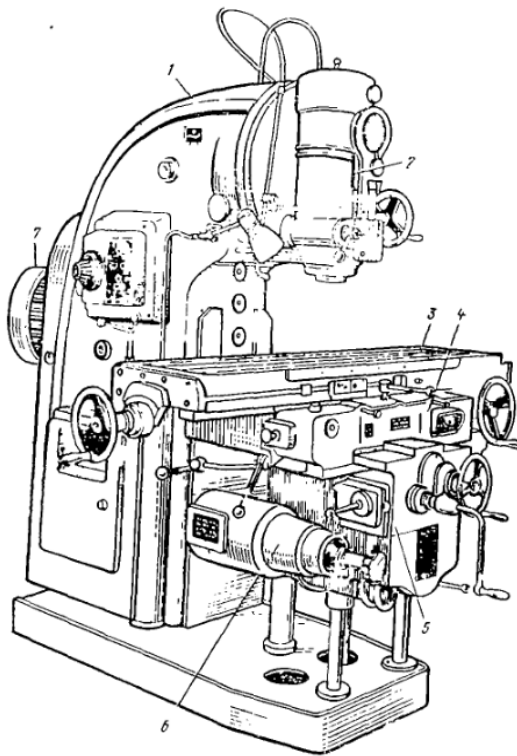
Вертикально-фрезерний станок модели 6H13
